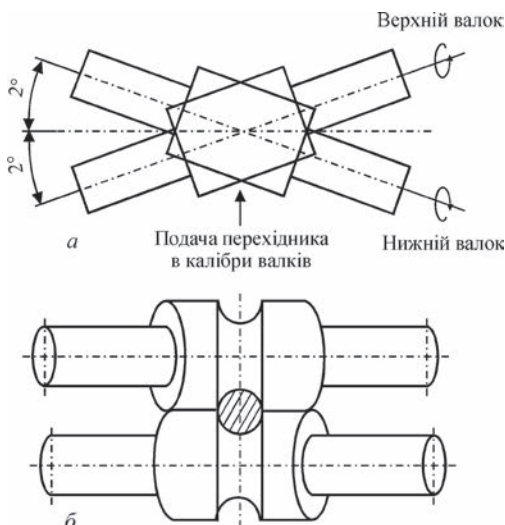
Схема розміщення валків: а — вид в плані; б — вид з торця
